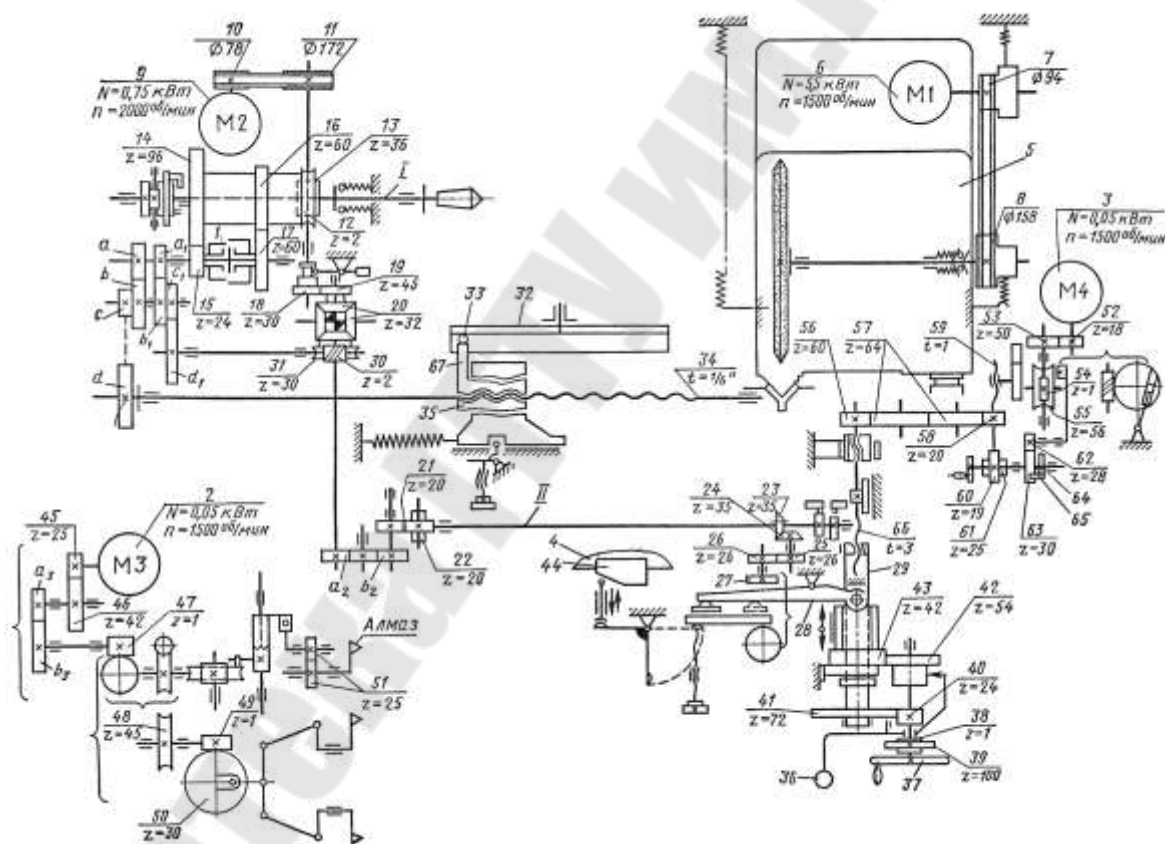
Принципиальная схема резьбошлифовального станка модели 5822М
